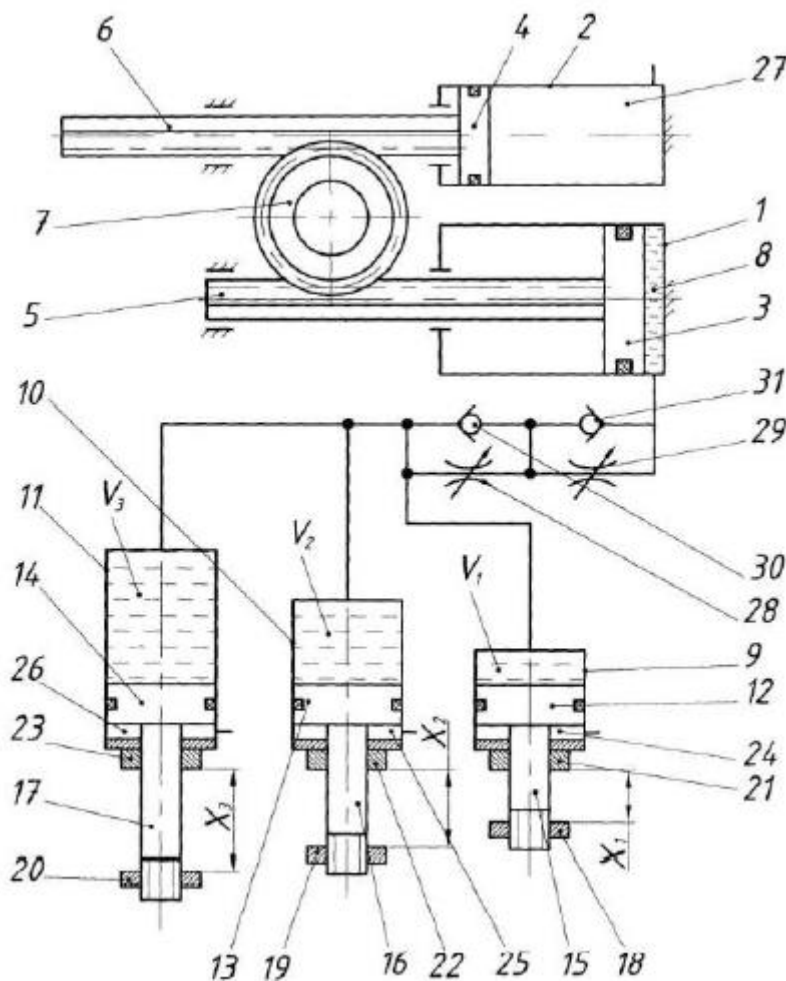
Багатопозиційний поворотний привід з цифровим керуванням
